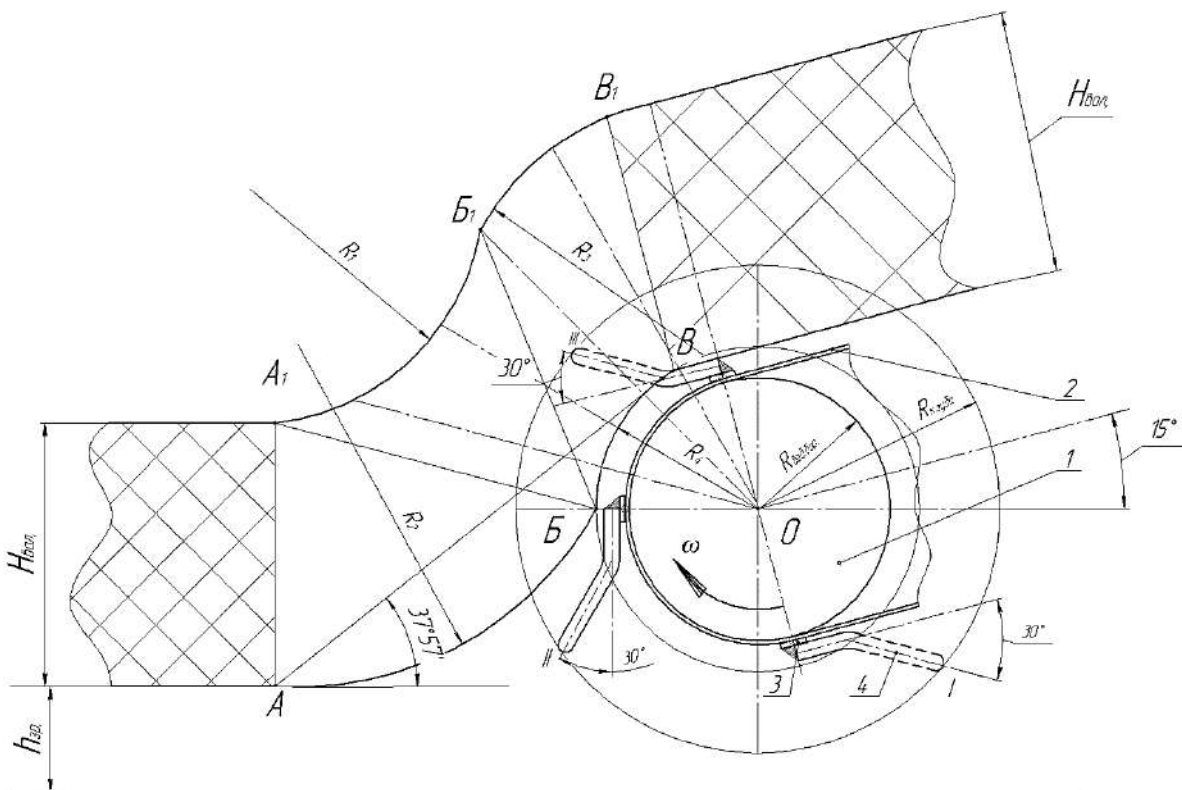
Схема до визначення умов відриву валка від поверхні поля з врахуванням форми зуба: 1 – ведений барабан; 2 – тягова стрічка; 3 – з'єднувальна планка; 4 – зуб
